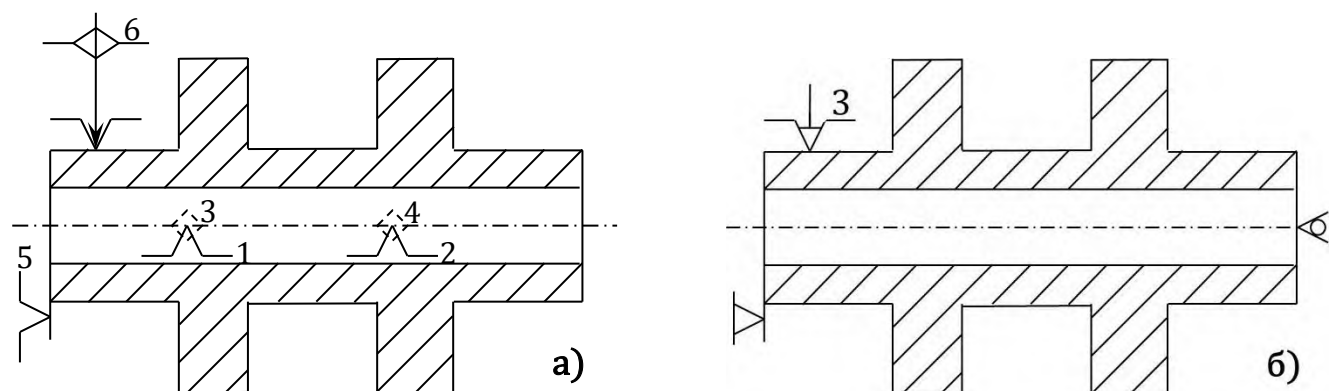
Схема установки деталі: а) схема базування деталі при токарній операції; б) схема закріплення деталі при токарній операції.
